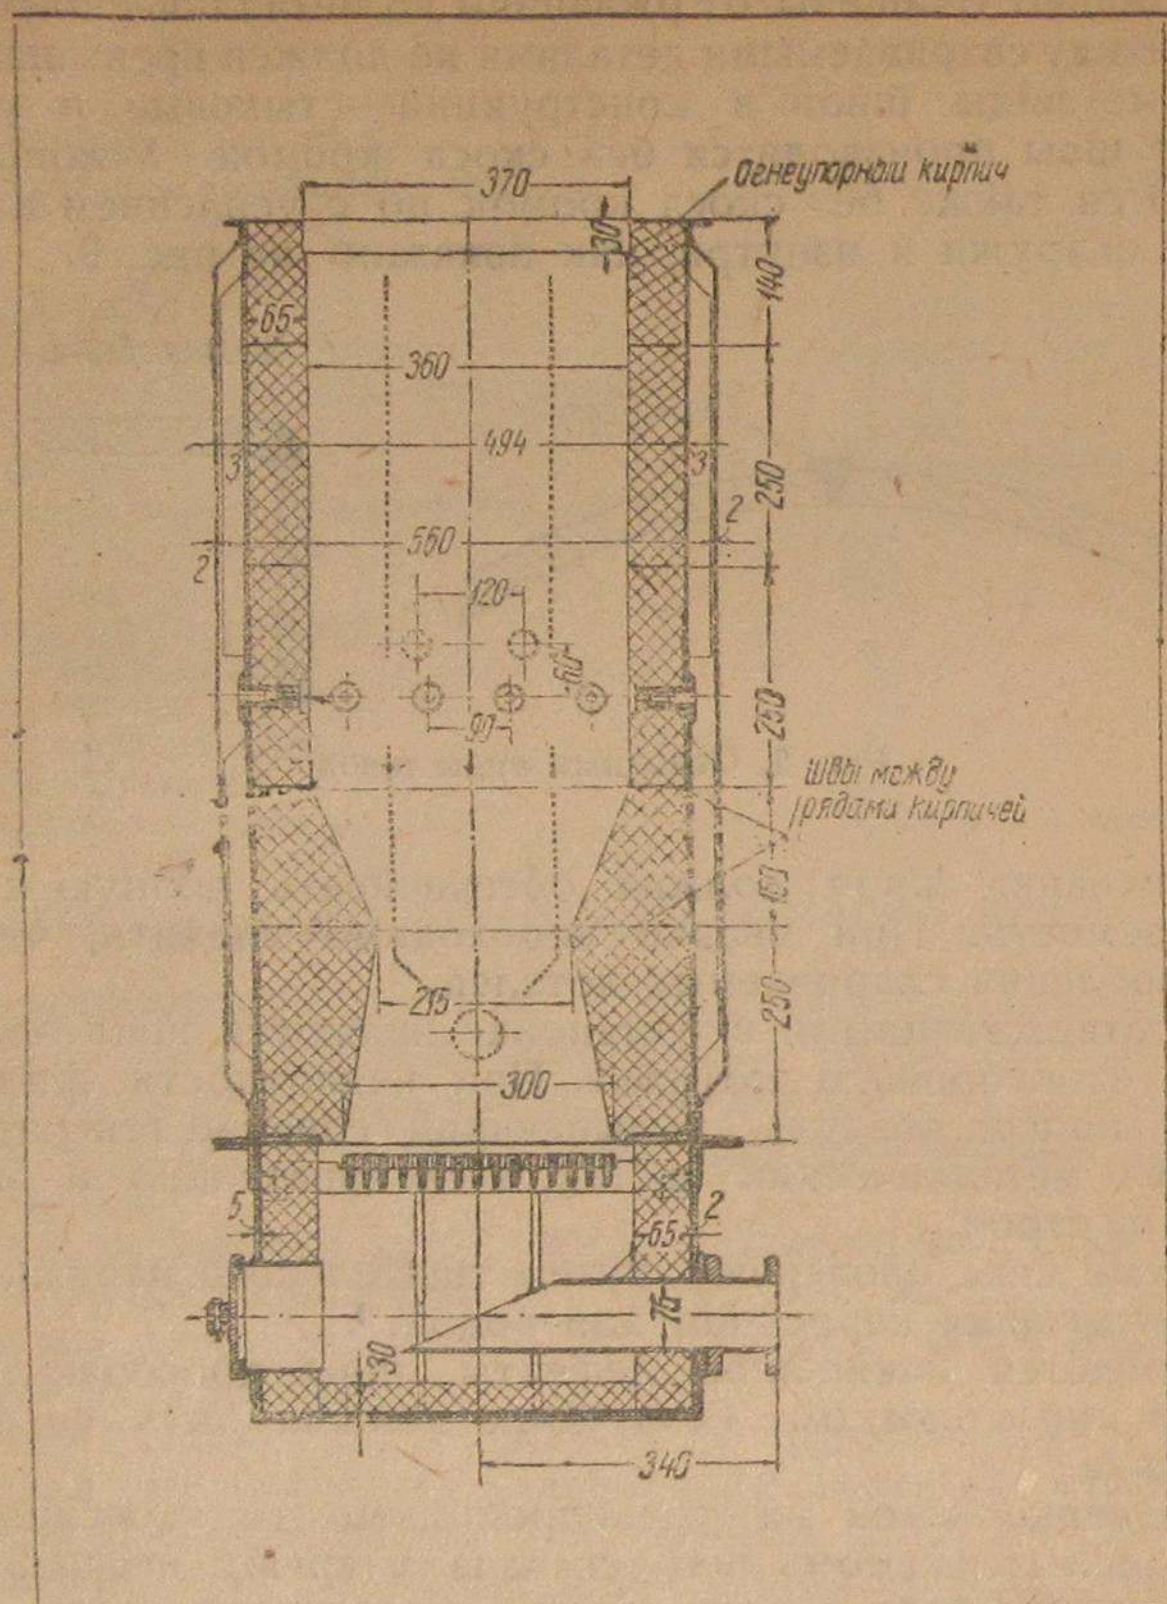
Внутренние очертания футеровки топливника и зольниковой камеры
